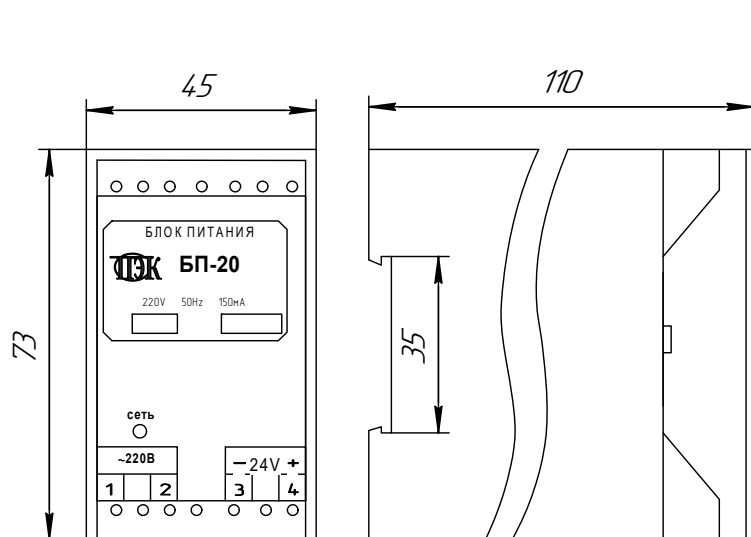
Габаритные размеры блока БП-20 (на DIN-рейке)
